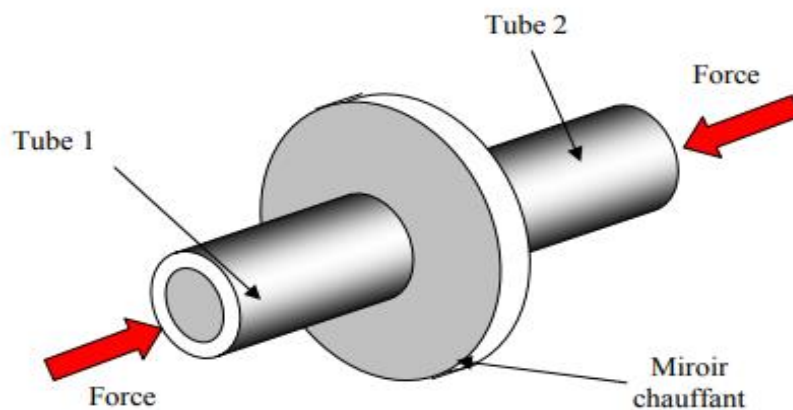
chauffage des tubes lors du soudage bout à bout.
